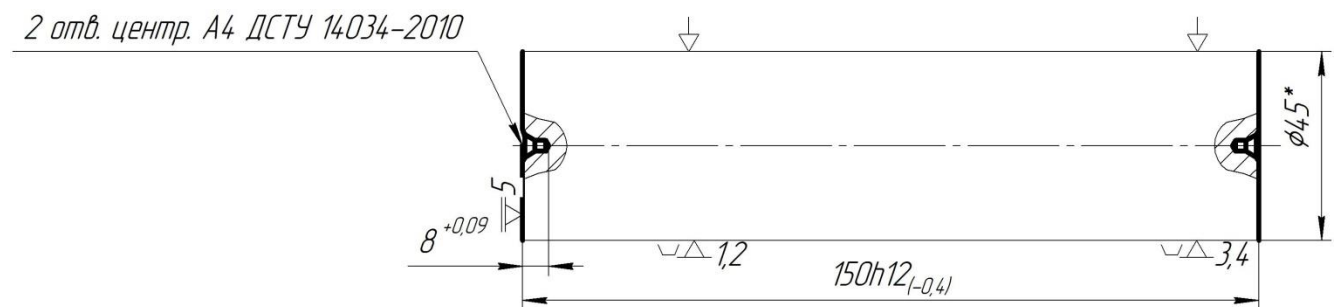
Схема установки заготовки на призми з притиском прихватами
